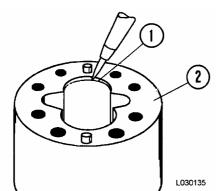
INSPECCION DE LA CAVIDAD DEL ENGRANAJE
